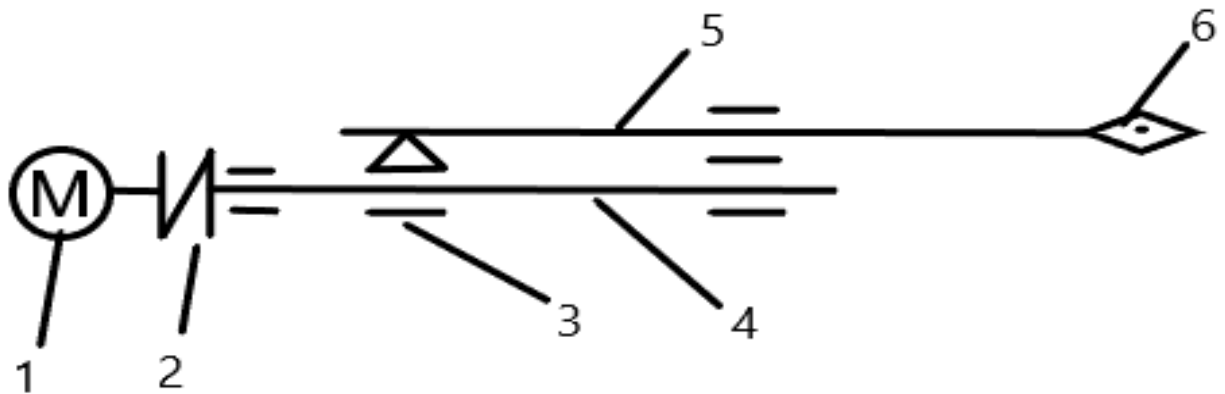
Кінематична схема механізму висування руки робота-маніпулятора
